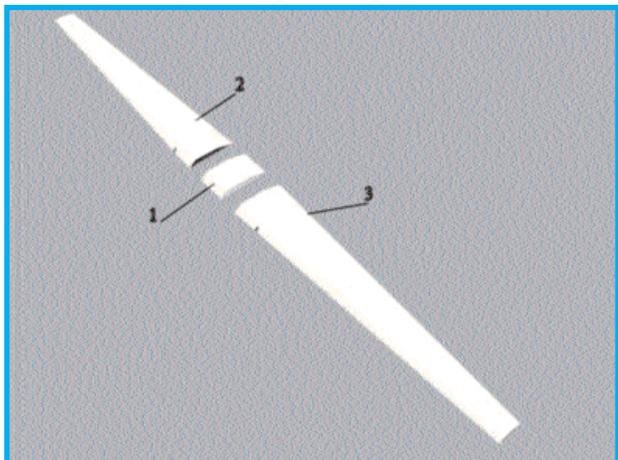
Компоновка консолей крыла: 1 — место крепления крыла; 2 — правая консоль крыла; 3 — левая консоль крыла
